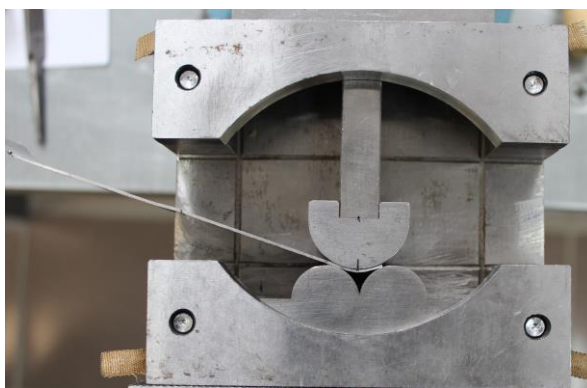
Подгибка кромки (заготовка под нагрузкой)
